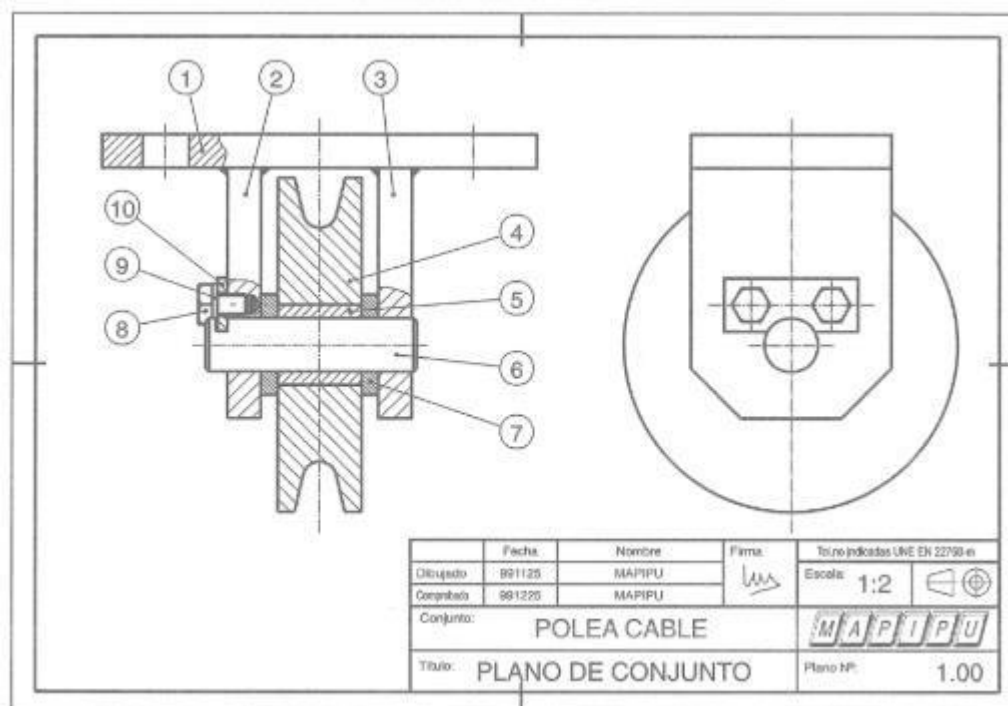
Ejemplo de plano aplicado a la ingeniería.
